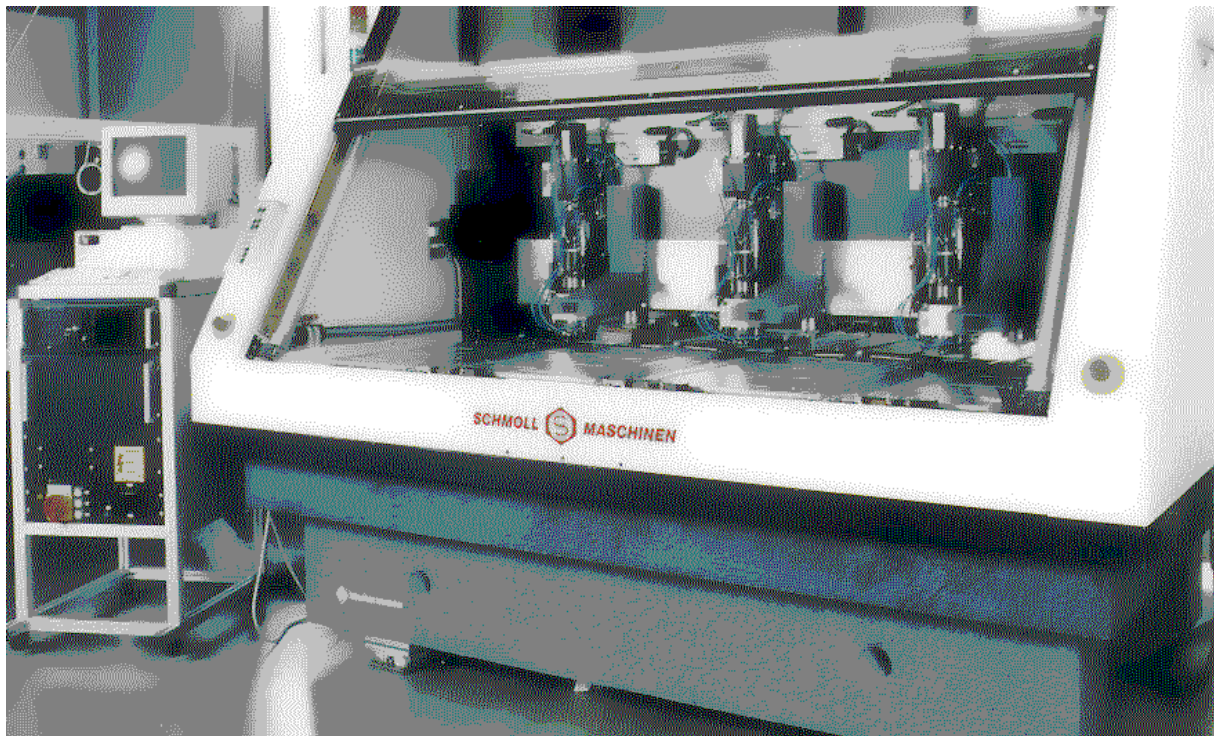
CNC-Fräsmaschine mit drei Fräsköpfen
